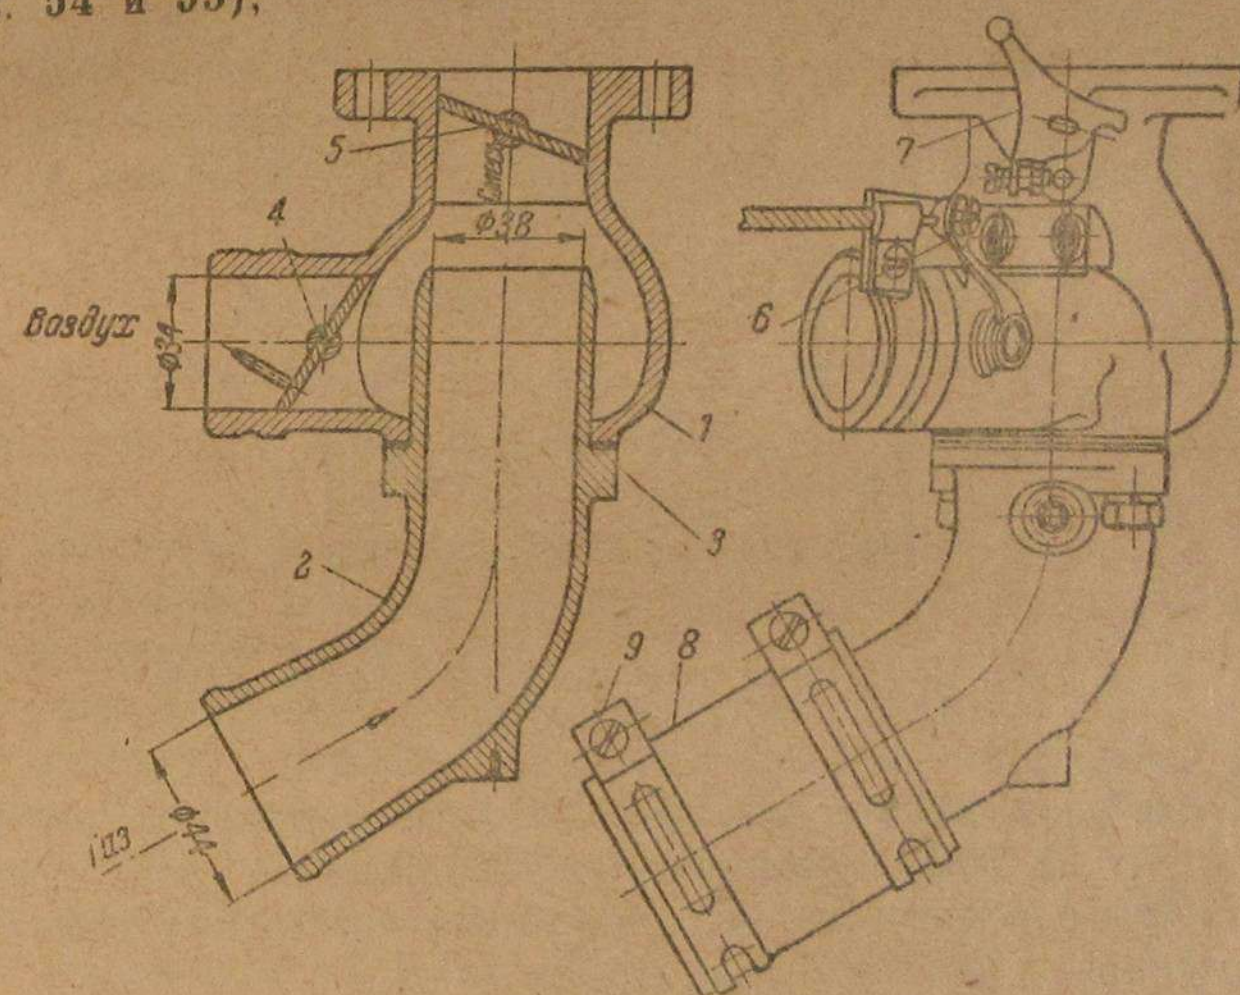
Смеситель газа двигателя ГАЗ-42: 1 — корпус смесителя, 2 — газовый патрубок, 3 — прокладка, 4 — воздушная заслонка, 5 — дроссельная заслонка, 6 — рычаг оси воздушной заслонки, 7 — рычаг оси дроссельной заслонки, 8 — соединительный шланг, 9 — хомуты
